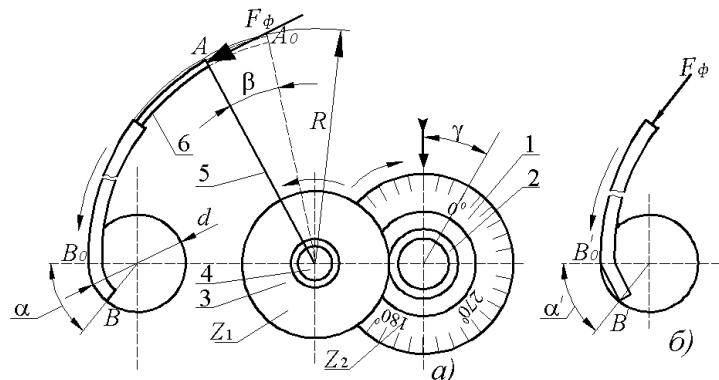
Розрахункова схема для визначення положення згортної карточки у формуючій фільтері
